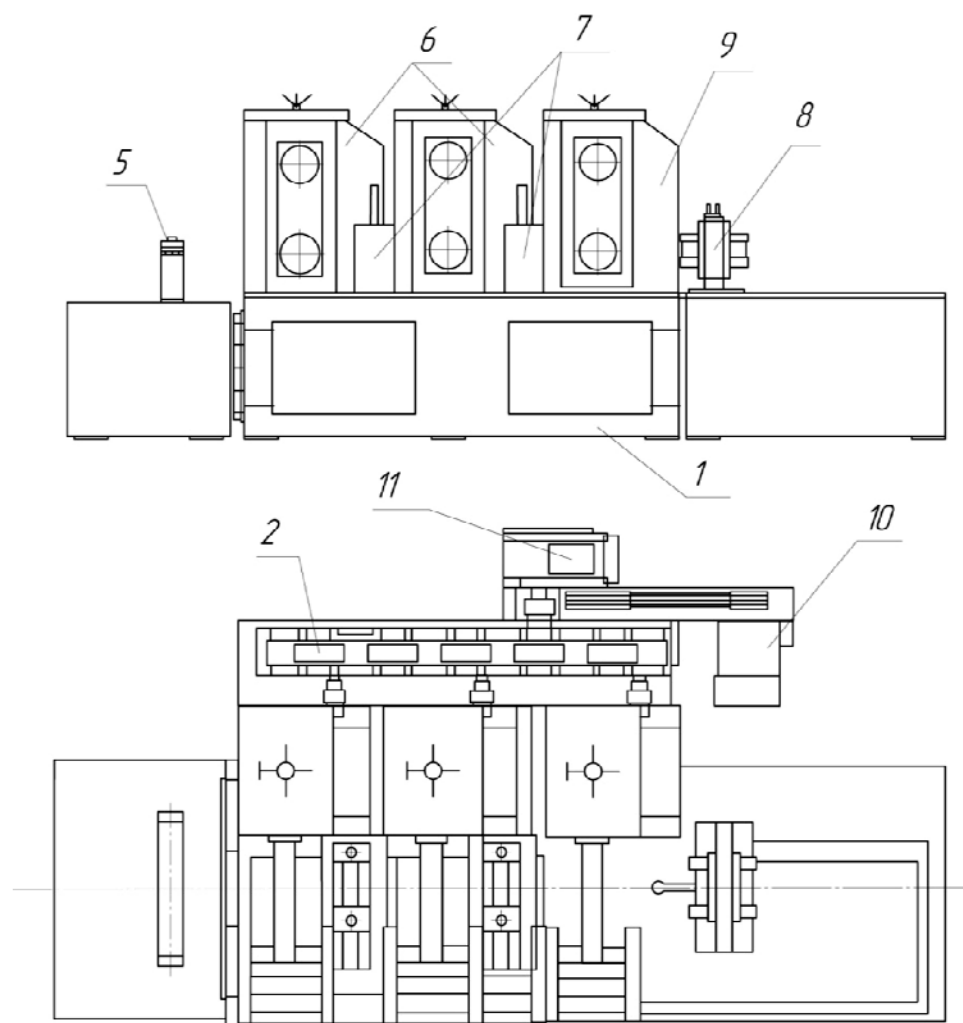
Гибочно-прокатный стан для изготовления стенки из листовой заготовки
